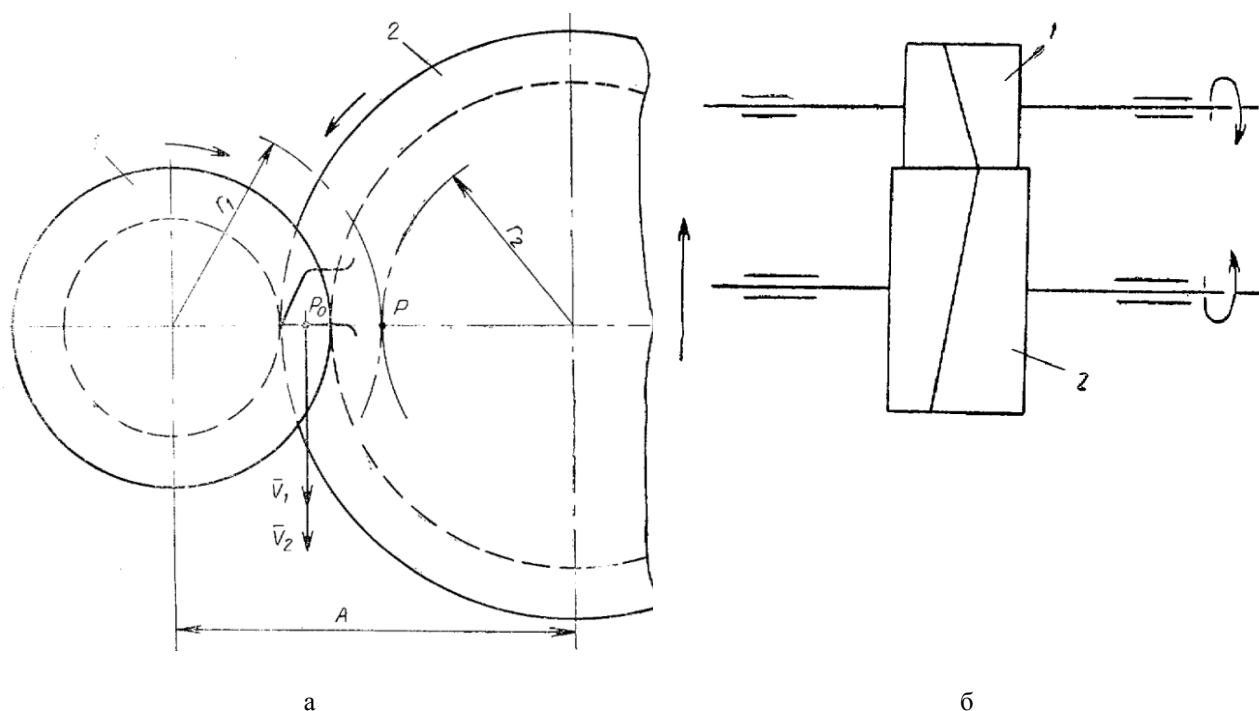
Способ фрезерования наружной резьбы методом огибания: а – схема зацепления фрезы и резьбы, б – кинематическая схема нарезания наружной резьбы.
